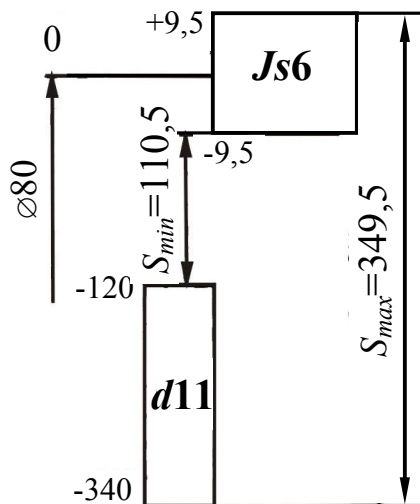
Схема полів допусків для посадки глухої кришки
